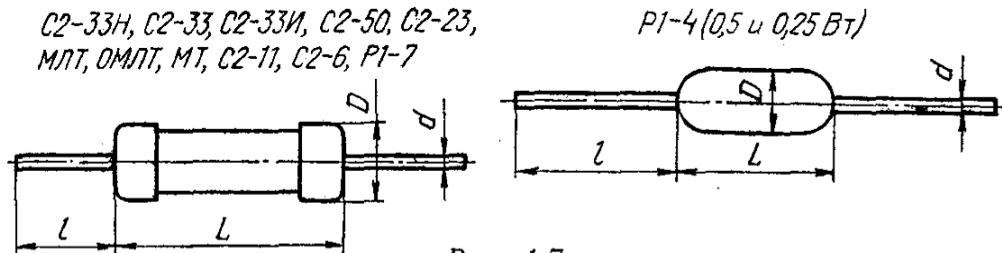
Конструкция и размеры резисторов общего назначения
